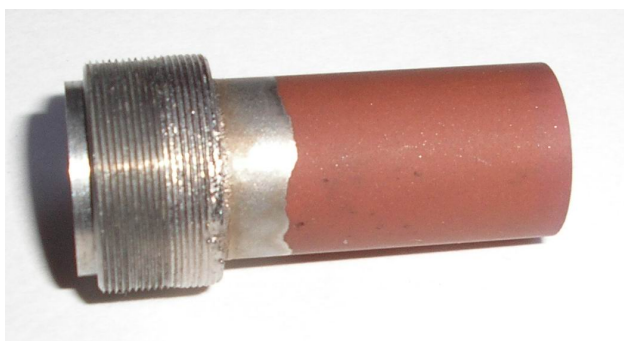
Металлокерамический корпус датчика линейных перемещений
